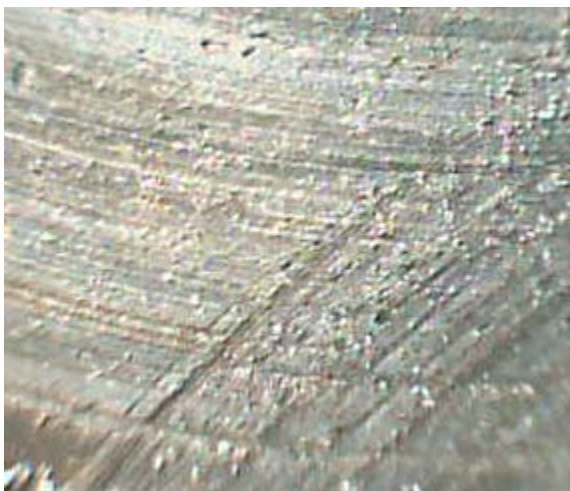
Поверхня тертя алюмінієвого корпусу шестеренного насосу із сплаву АЛ-9 в парі з вуглецевою сталлю
